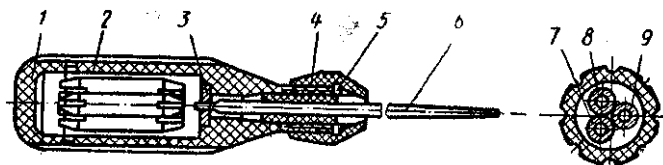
Рукоятка для закріплення напилків з циліндричними хвостовиками
